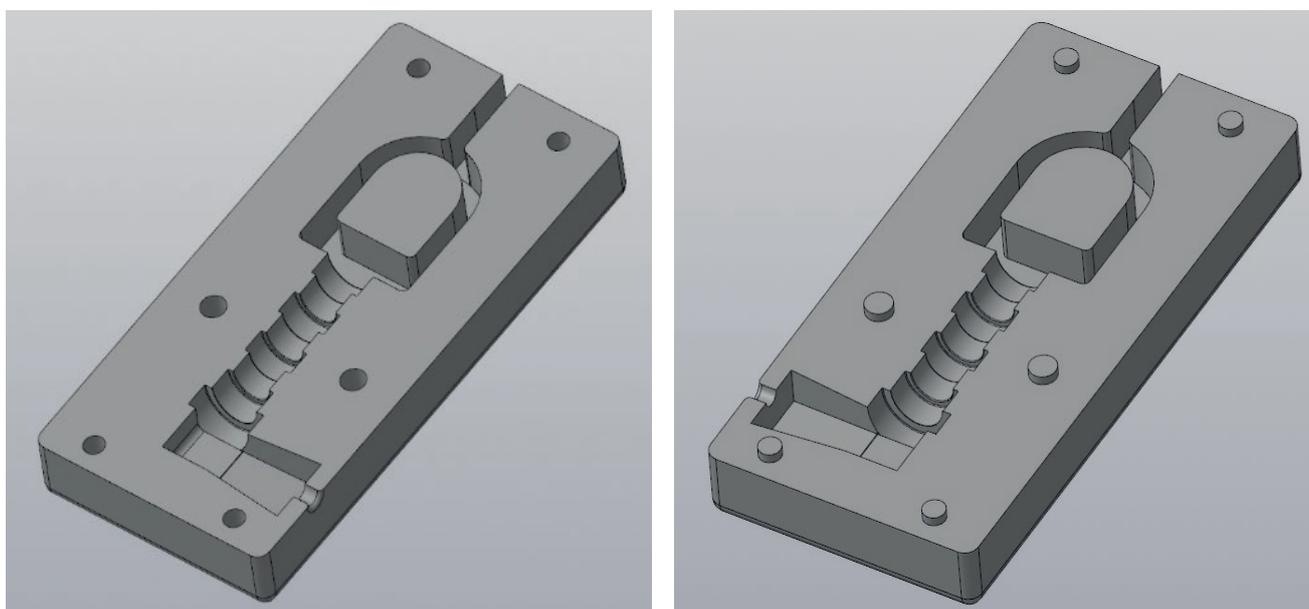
Части пресс-формы для отливки «Прижим»: *а, б* – нижняя и верхняя полуформы
